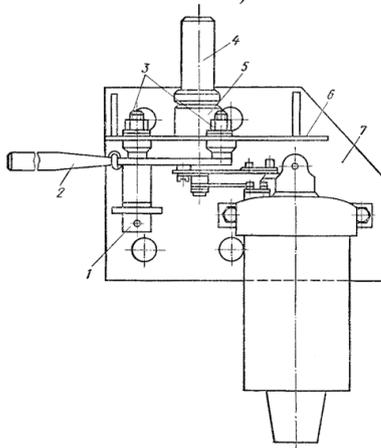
Привод ПРН-110: 1 — пружинная защелка, 2 — рычаг, 3 — чашечки, 4 — вал, б — втулка. 6 — полка, 7 — основание
